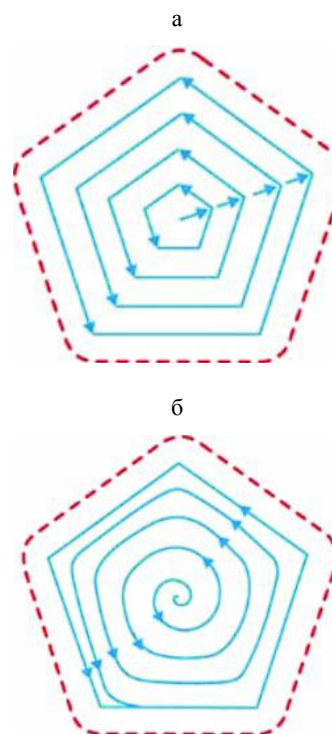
Схемы траекторий движения инструмента: а – с резким изменением направления; б – плавное движение
